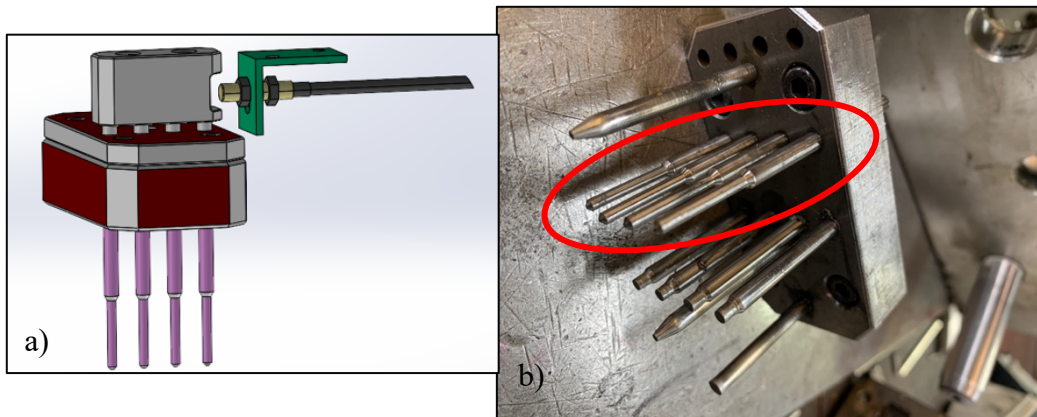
Primeiro sensor: a) Sistema de paragem da máquina projetado e b) Punções de deteção já maquinados e montados.
